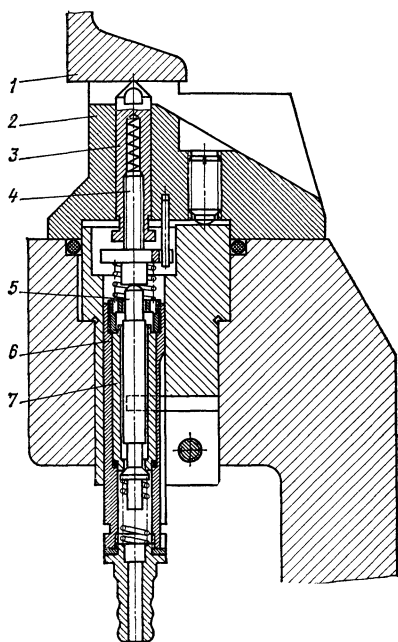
Устройство для контроля прилегания обрабатываемых деталей к базовым элементам приспособления:
